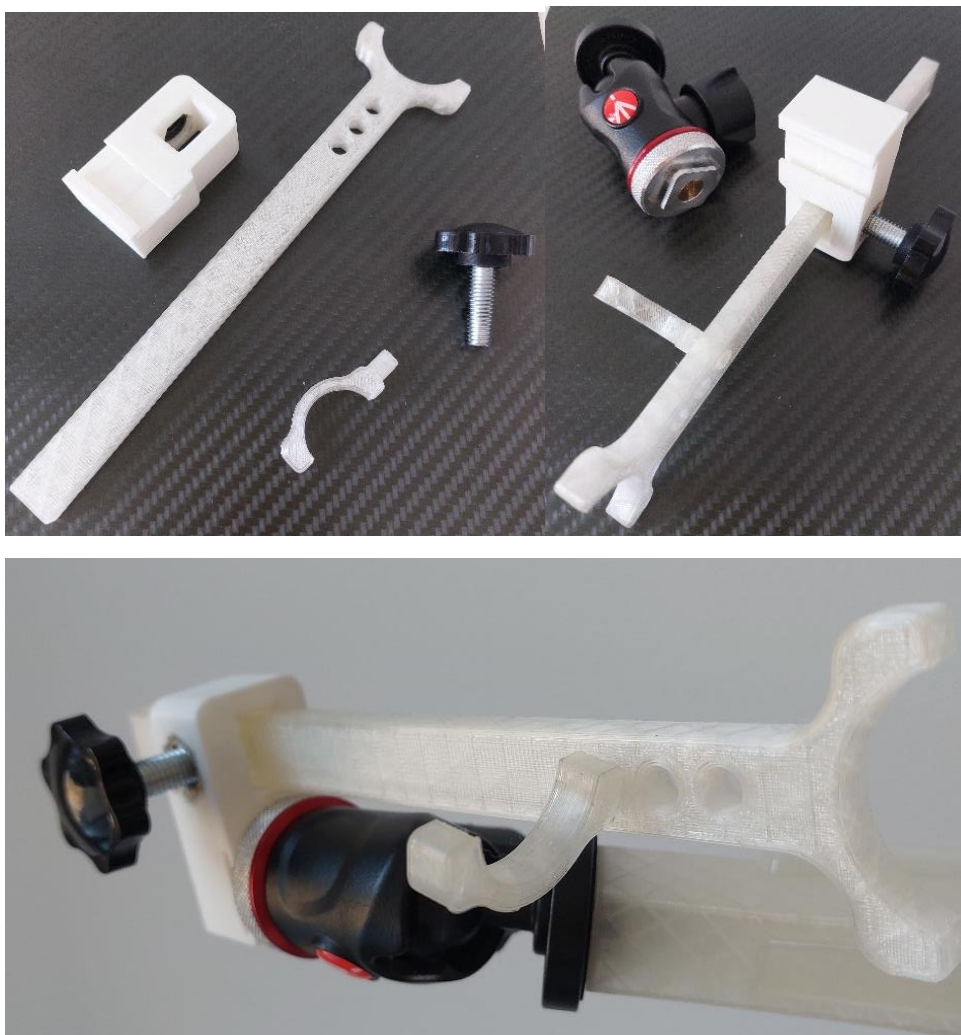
Ensamblaje de rótula, zapata y posicionadores de pulgar y palma.
